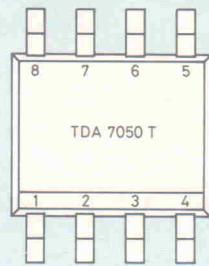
Draufsicht. Die abgeschrägte Oberkante kennzeichnet die Einbaulage.
